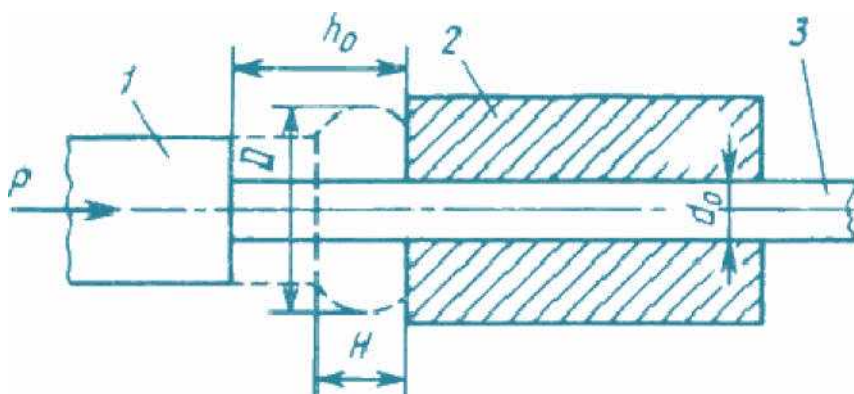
Схема процесу висадки: 1-пуансон; 2-матриця; 3-заготовка.
